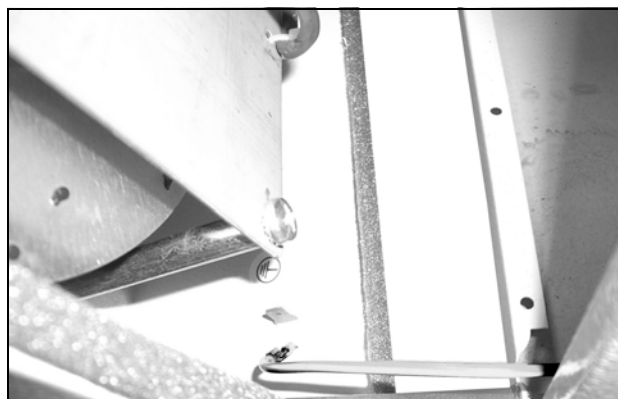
Provléknutí kabelu displeje kabelovou průchodkou
